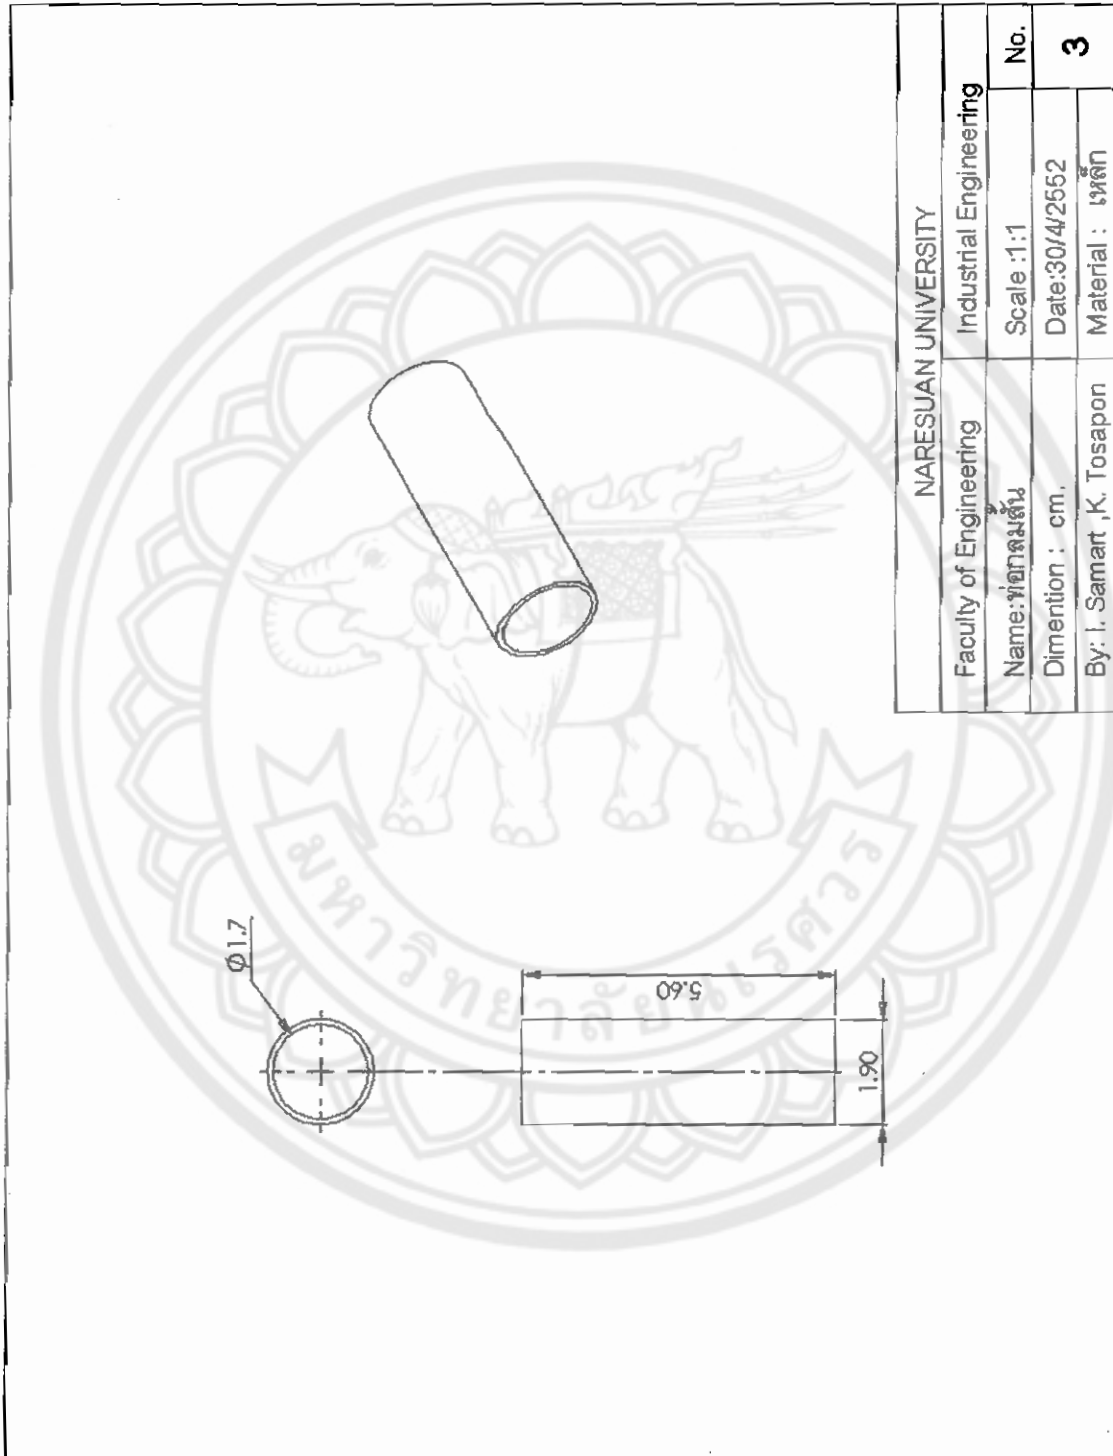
แสดง Assembly Drawing จักรวางคัลัม
